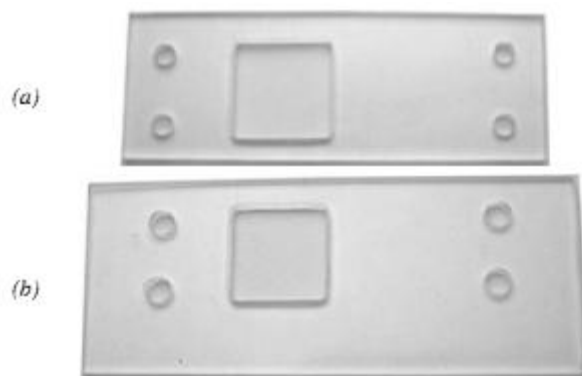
Moldes utilizados para testar o método num Palm PDA. a) Molde inicial que ficava assente apenas na área de texto do PDA. b) Molde seguinte que ficava suportado apenas no chassis do PDA.
